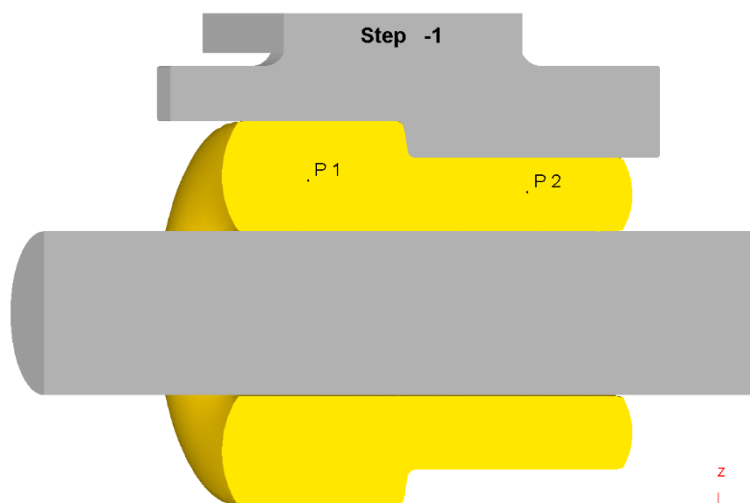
Ескіз заготовки для моделювання процесу розкочування при одночасному деформуванні виступу й уступу
